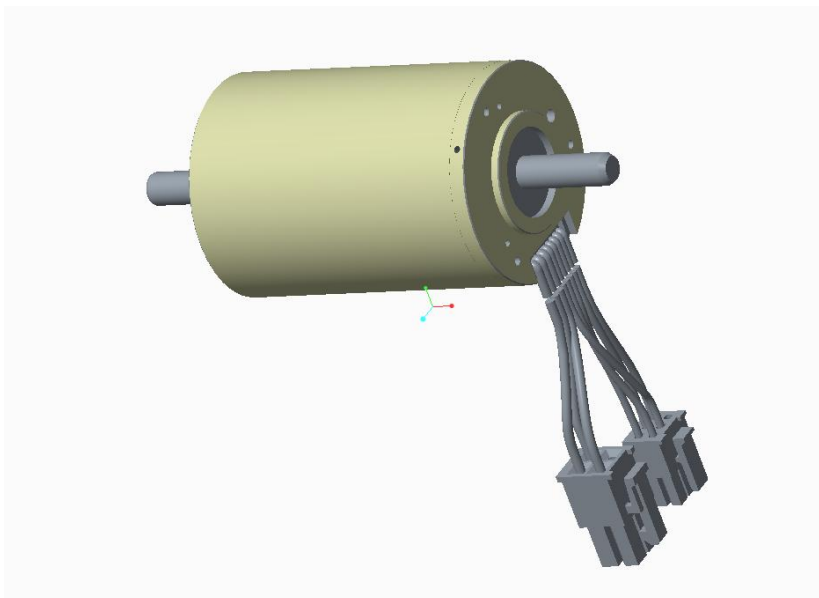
Motor Maxon EC-max 40, 3D CAD
